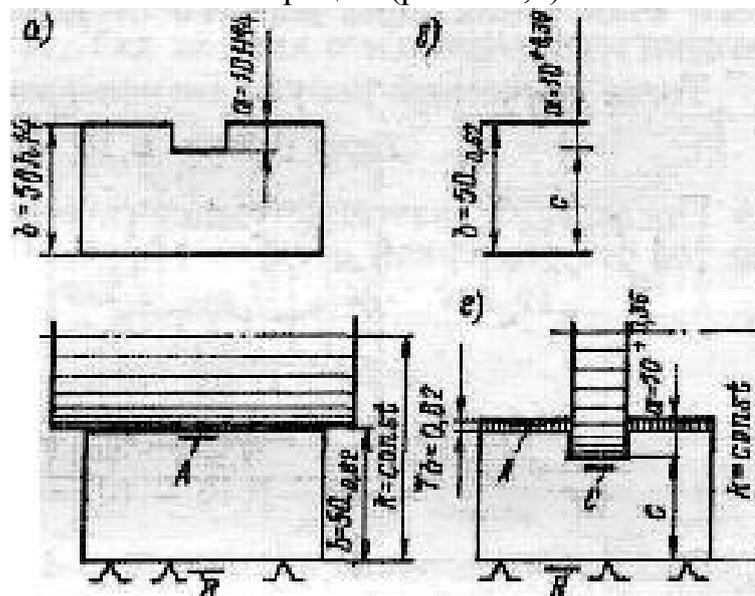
Фрезерование паза от опорной технологической базы В, не совпадающей с конструкторской
